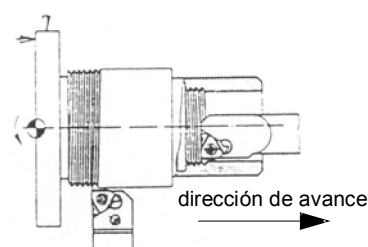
roscado a la izquierda con el husillo de la máquina girando a la derecha
